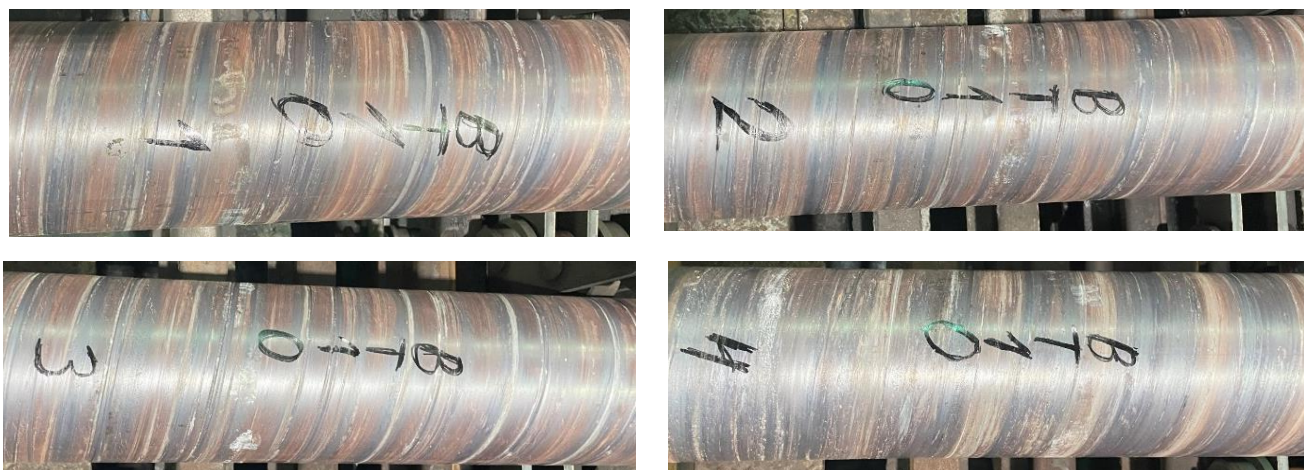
Внешний вид труб из сплава ВТ1-0
